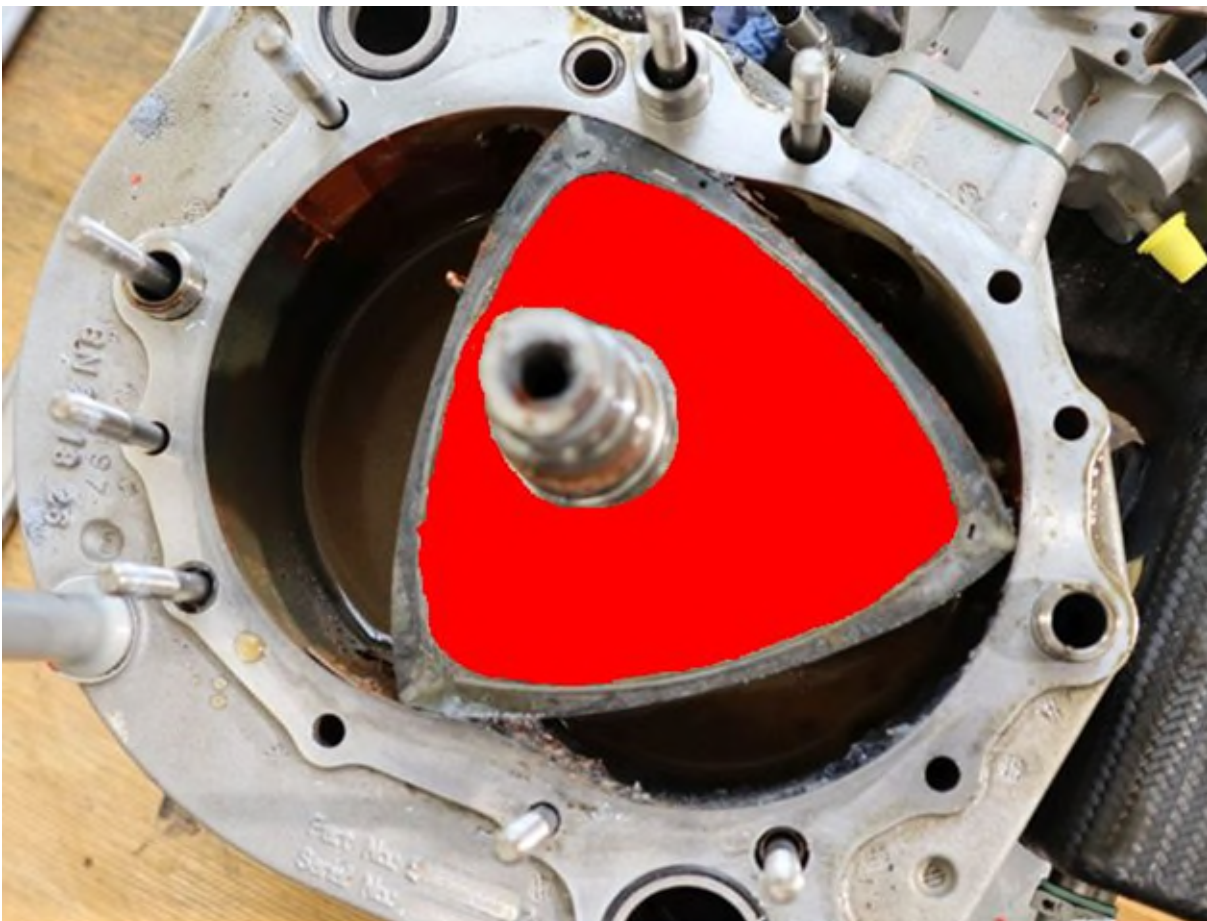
Blockierter Rotationskolben im Motorgehäuse
